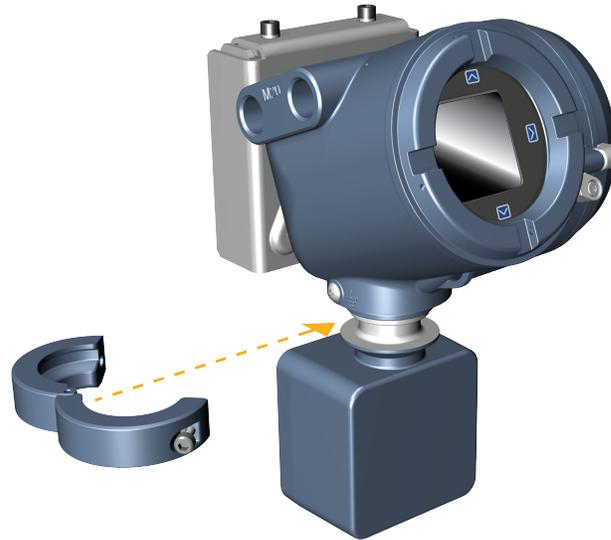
Rotación de la caja de conexiones del cableado del sensor
